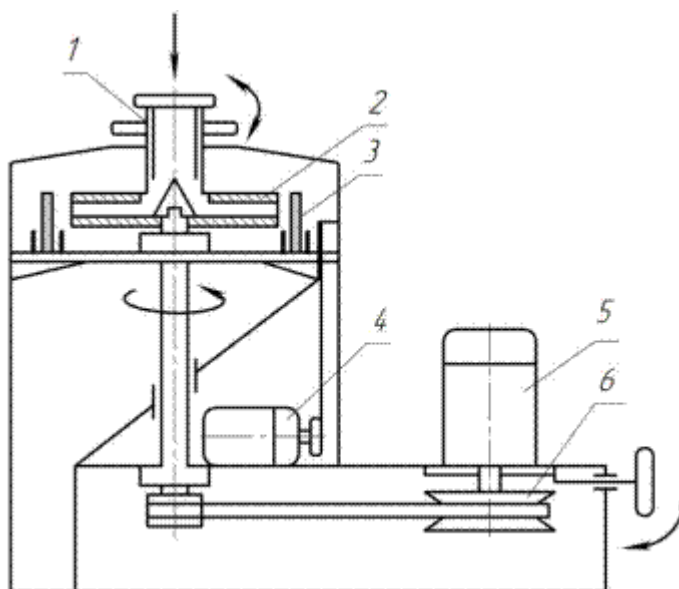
Схема робочих органів луцильника «Стратопакт» фірми «Бюлер»: 1 – приймальна труба; 2 – лопатковий ротор; 3 – ударна дека; 4 – мотор-редуктор; 5 – електродвигун; 6 – варіатор швидкостей
